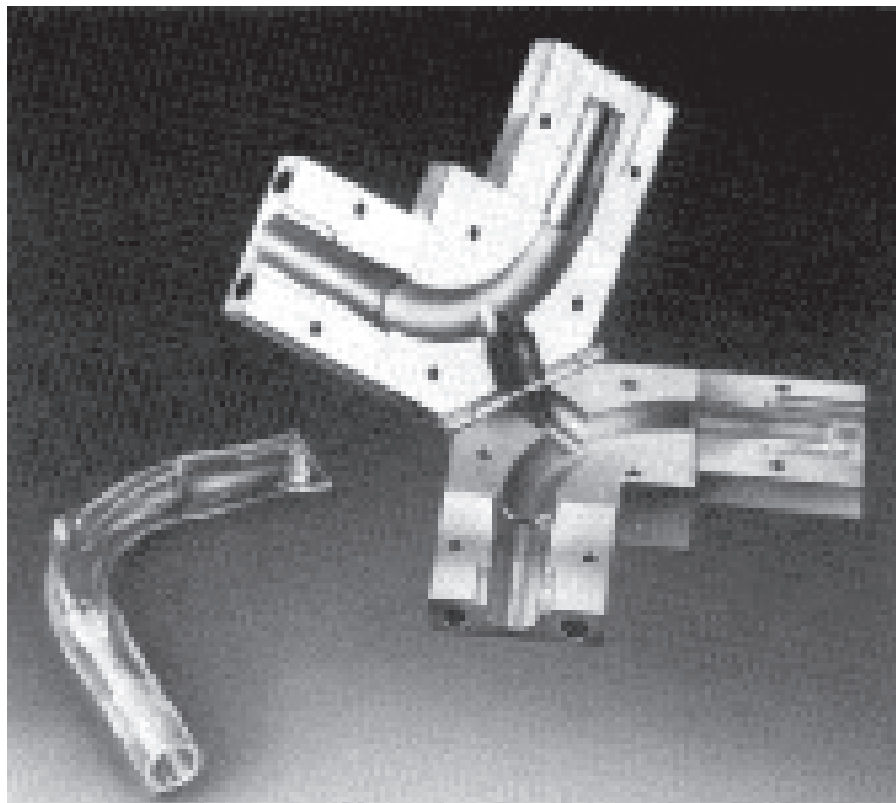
Druckluft-Formwerkzeug für Rohrkrümmer
